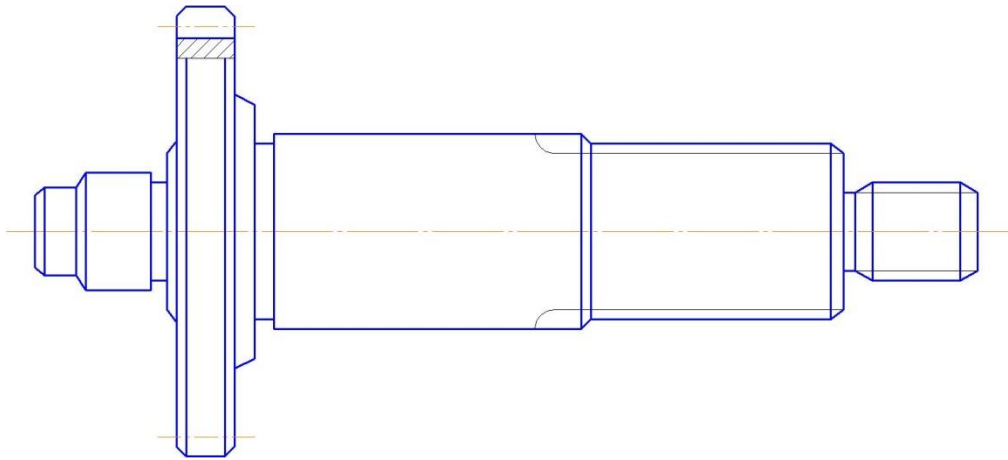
Загальний вид валу привода валу відбору потужності
